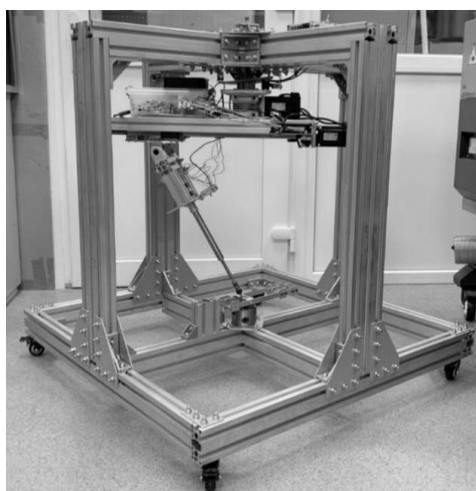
Станок для взаимной сферической притирки шаровых шарниров
